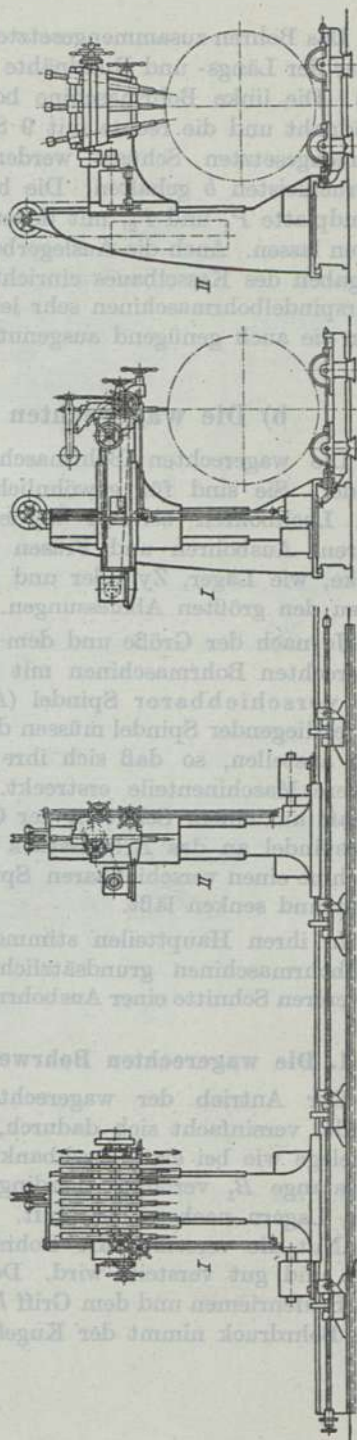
bis 459. Plan einer Kesselbohrmaschine.
